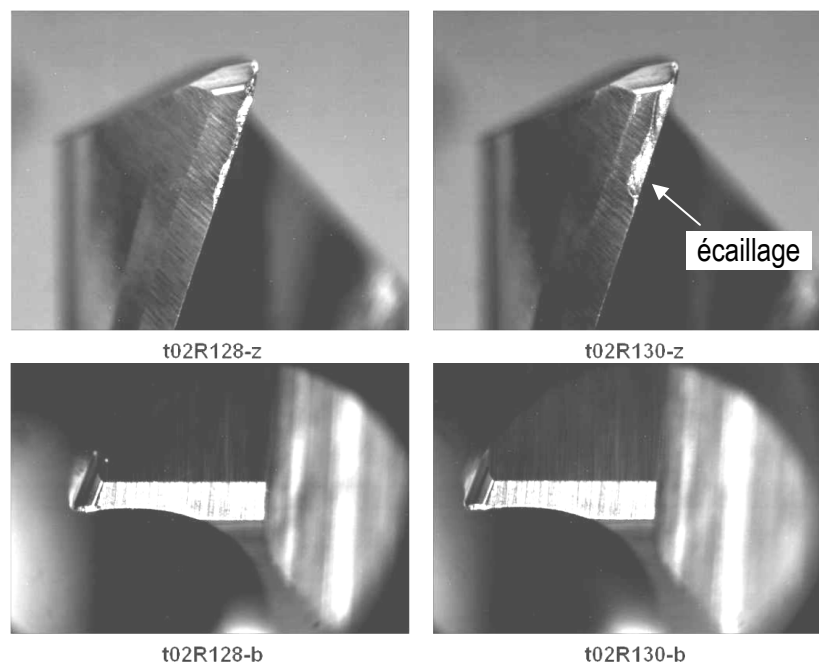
Ecaillage important (entre les passes 128 et 130, essai E)
